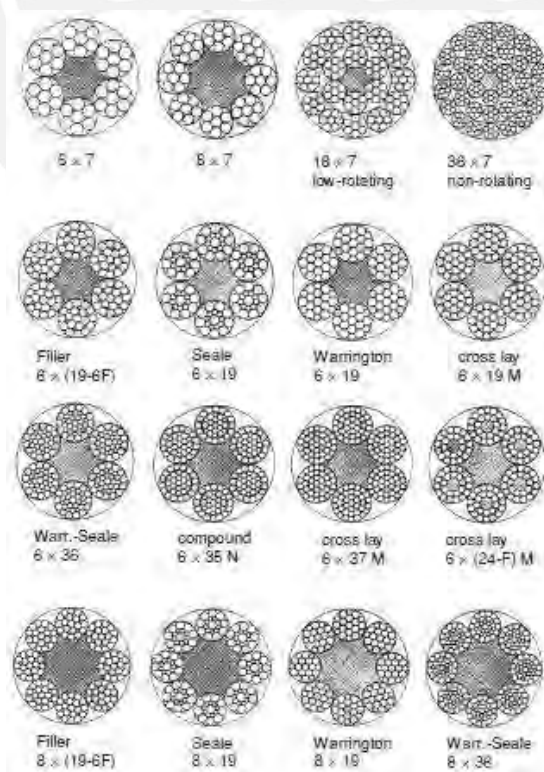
Ejemplos de estructura transversal de cables de acero con alma de fibra [5, p. 37]
